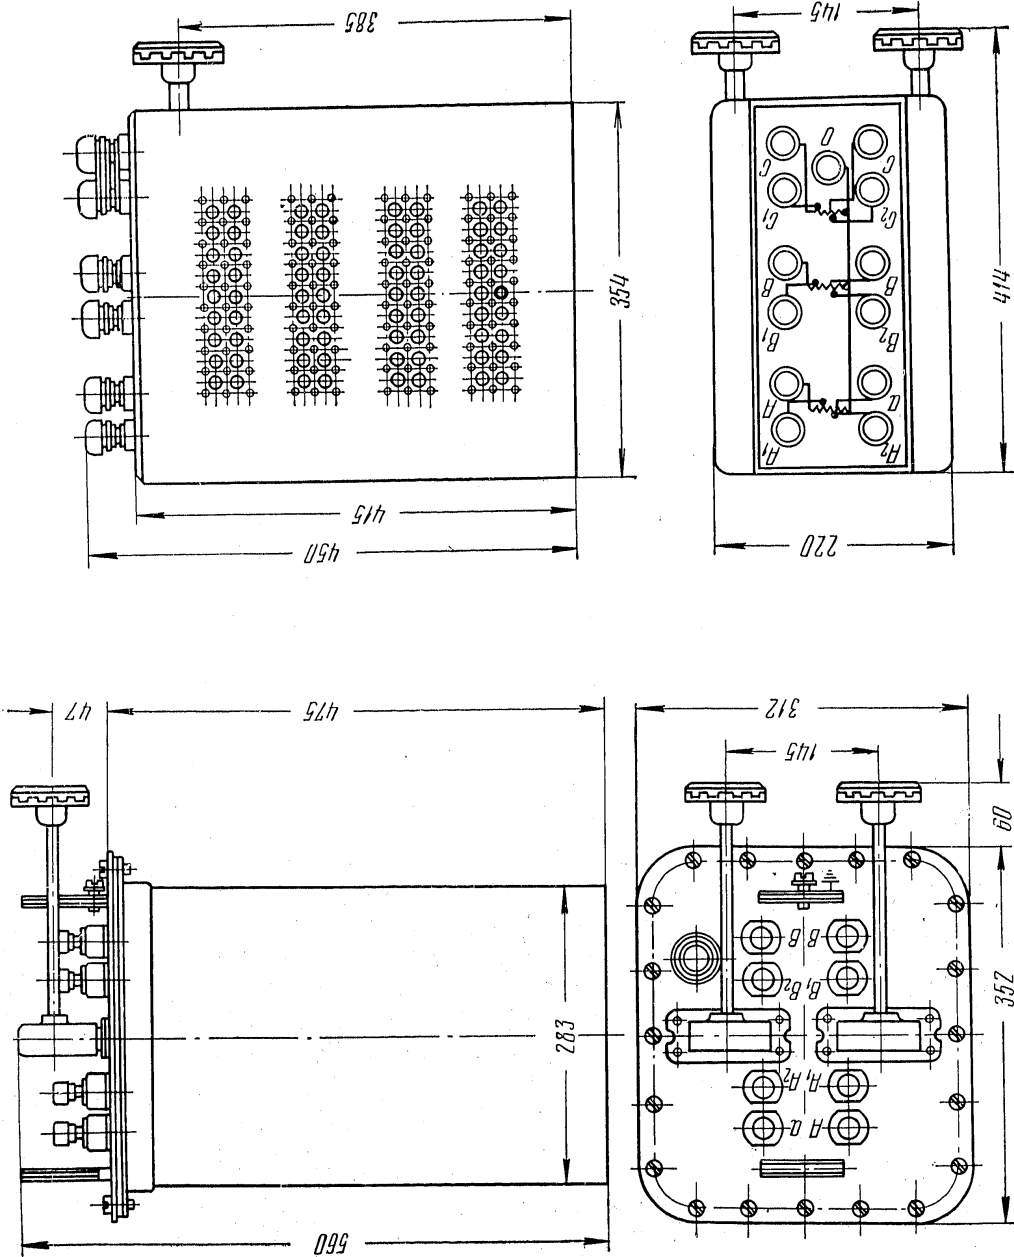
Габаритные размеры трехфазного масляного вариатора РНТ-220-6 на 6 кВа
